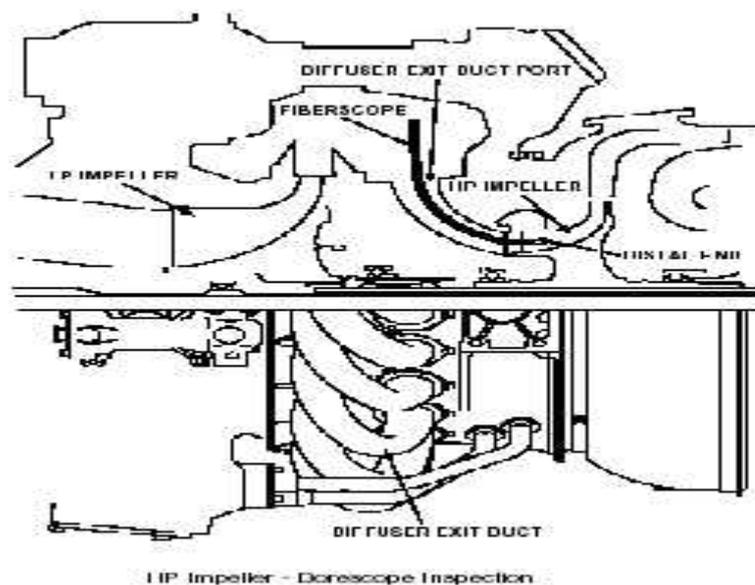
Inspection boroscopique du compresseur HP.
